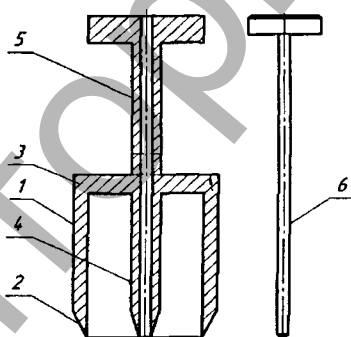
Устройство для изготовления трубчатых obturаторов:
